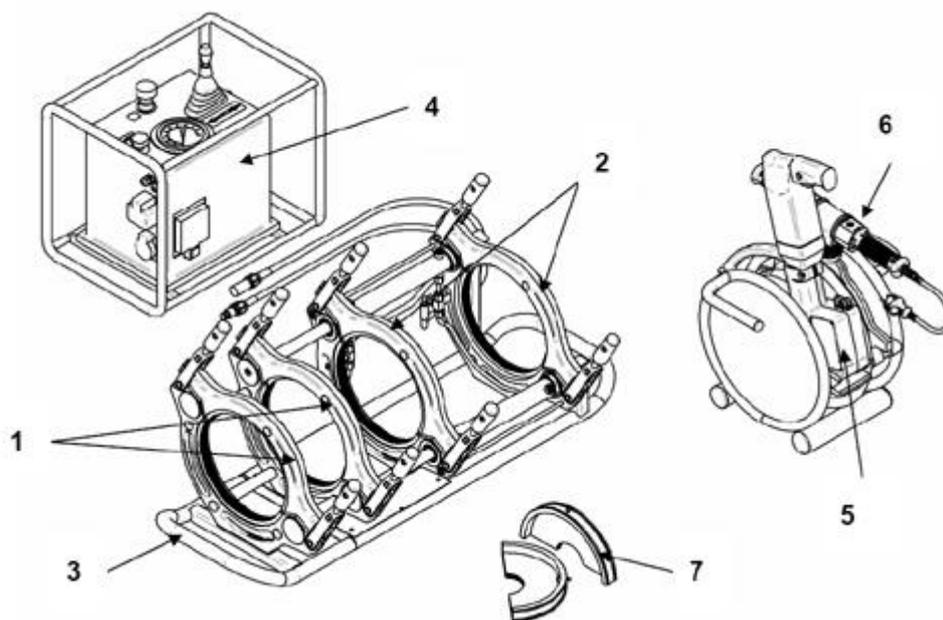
Состав оборудования для стыковой сварки:
